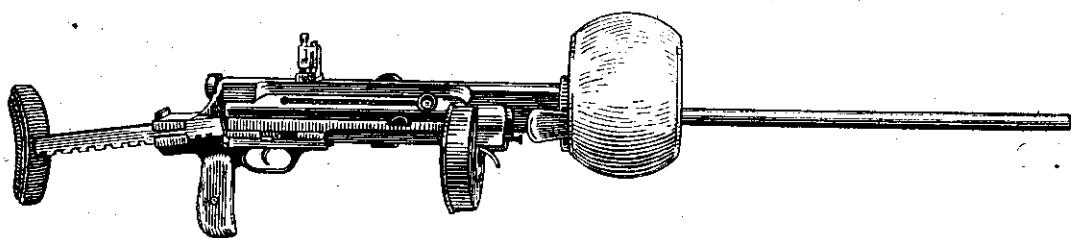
Общий вид танкового малокалиберного пулемета в шаровой установке.
